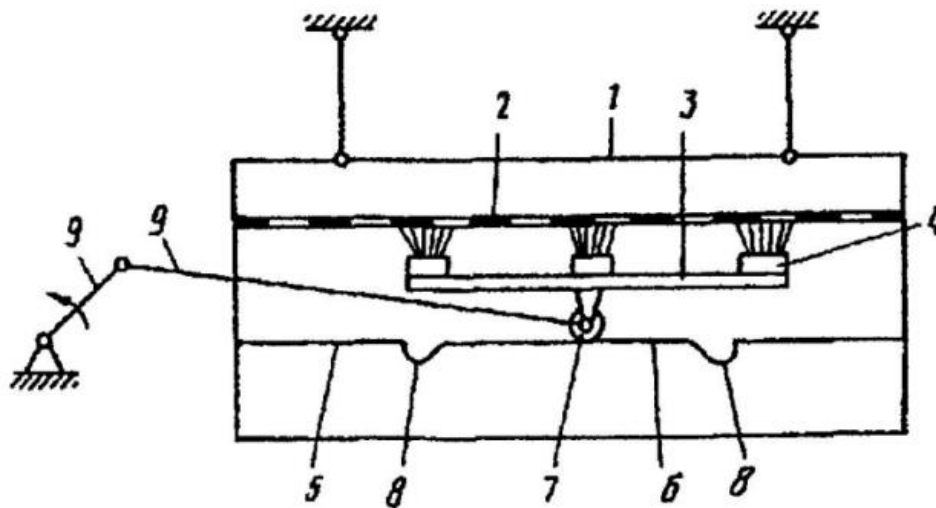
Активний повзунковий (коливальний) щітковий апарат для очистки отворів решіт: 1 – решітний стан; 2 – сито; 3 – повзун щітковий; 4 – щіточка; 5, 6 – смужки; 7 – ролик; 8 – пази кінцеві; 9 – коливальник;
